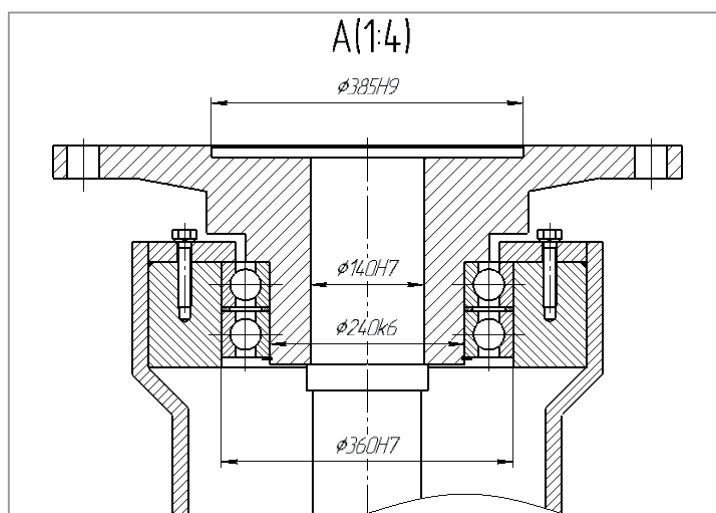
Новая конструкция опорной части стойки крышки РНП
